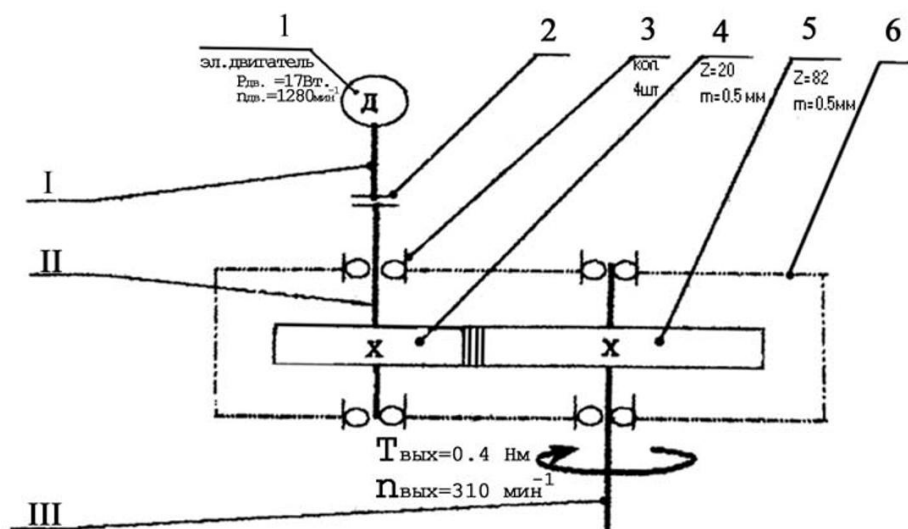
Кинематическая схема механизма: 1 – электродвигатель; 2 – муфта; 3 – опора качения; 4 – шестерня (ведущее зубчатое колесо); 5 – ведомое зубчатое колесо; 6 – корпус; I – вал электродвигателя; II – ведущий (входной) вал редуктора; III – выходной вал редуктора.
